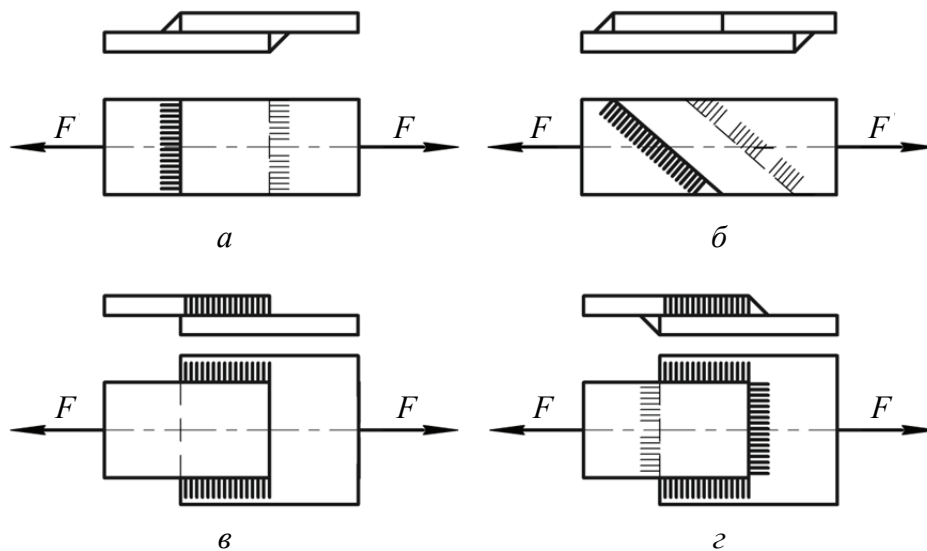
Сварные швы по направлению нагрузки:
